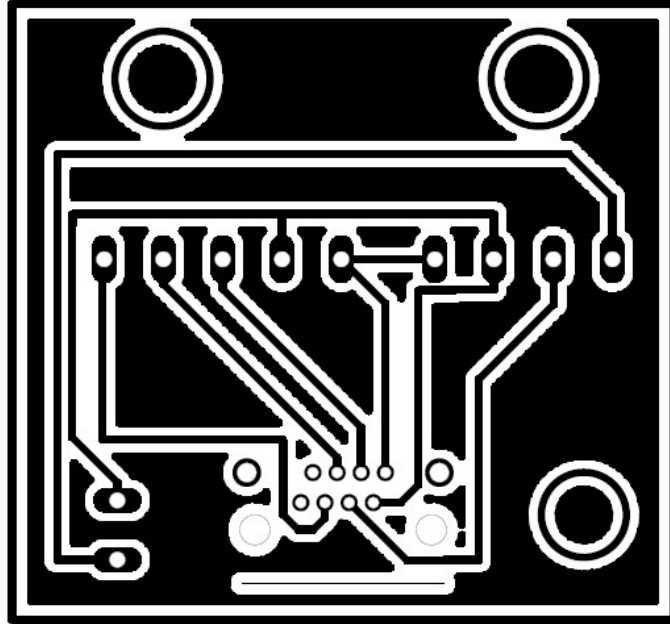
Segundo diseño de PCB en formato para imprimir.
